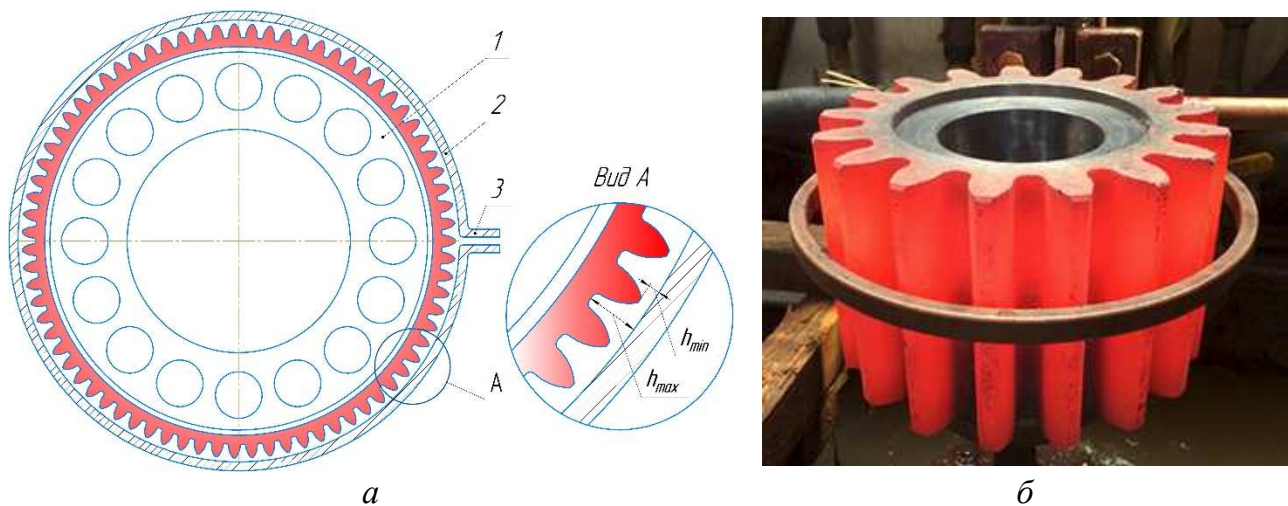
Цилиндрический индуктор: а – охват витком индуктора зубчатого венца; б – пример нагрев шестерни; 1 – венец; 2 – виток; 3 – отвод для провода
